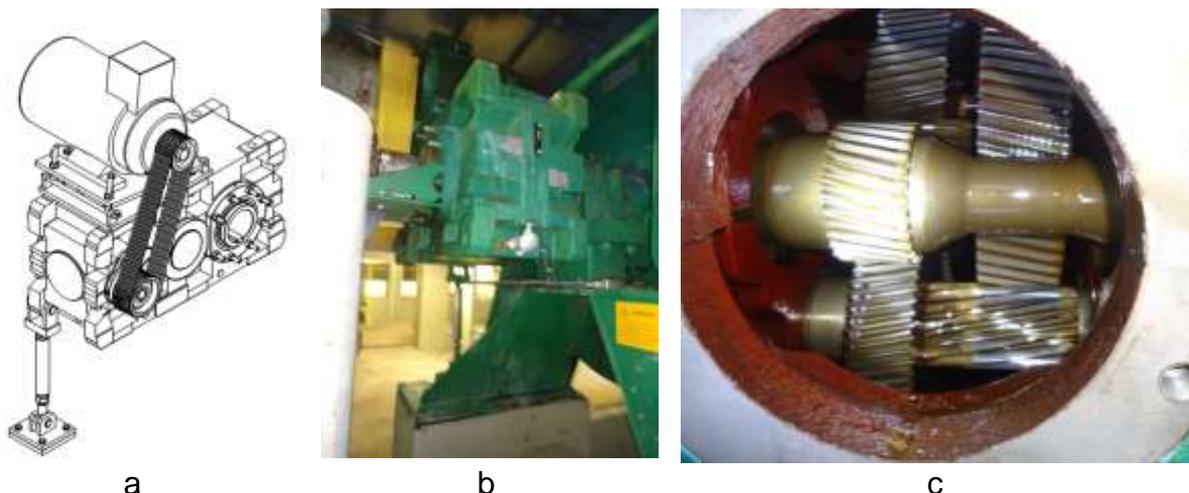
Conjunto motriz do secador de disco. a - Desenho completo da montagem do acionamento. Fonte: Adaptado de Harslev (p. 48). b - Foto do acionamento na instalação. c - Foto das engrenagens e eixos pela porta de inspeção lateral.
